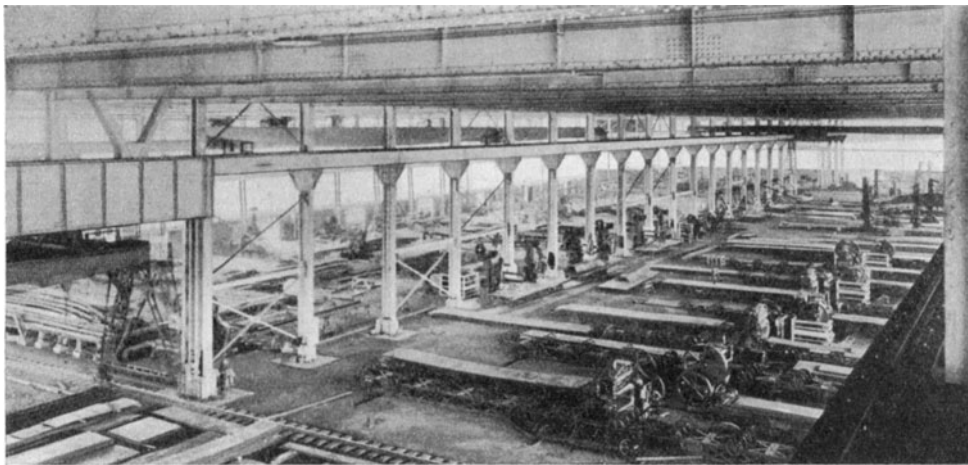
Schiffbauhalle der New York Shipbuilding Co.
